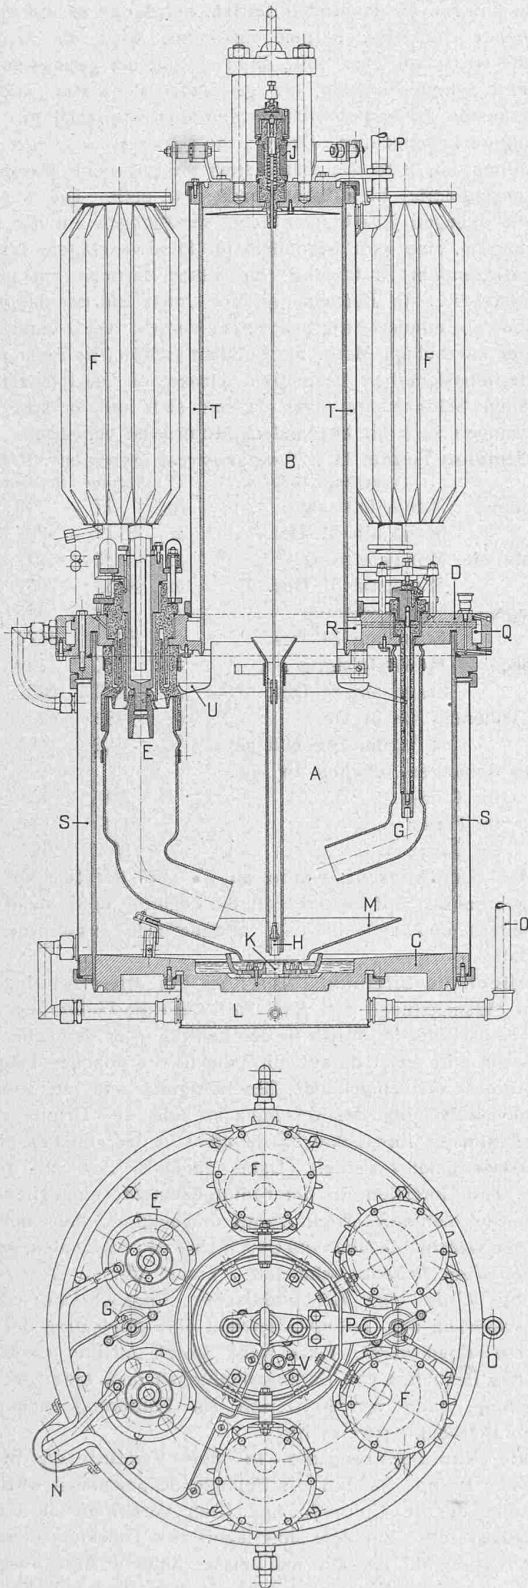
Quecksilberdampf-Gleichrichter mit gekühlten Anoden, für max.  $500 \text{ Amp}$ . — Querschnitt und Grundriss. — 1:15.
